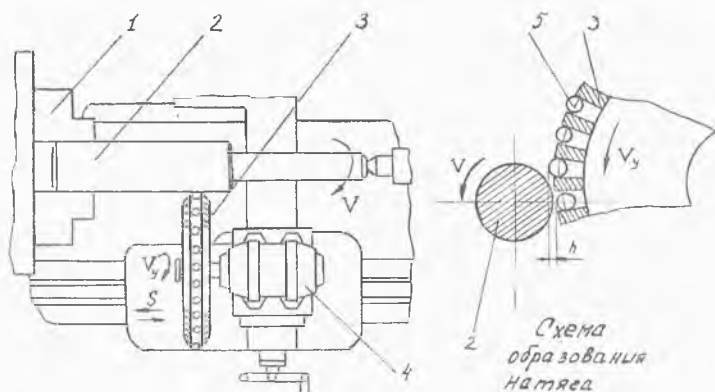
Схема обработки деталей ротационным упрочнением на токарно-винторезном станке: 1—патрон станка; 2—деталь; 3—ротационный упрочнитель; 4—электродвигатель; 5—шарики упрочнителя
